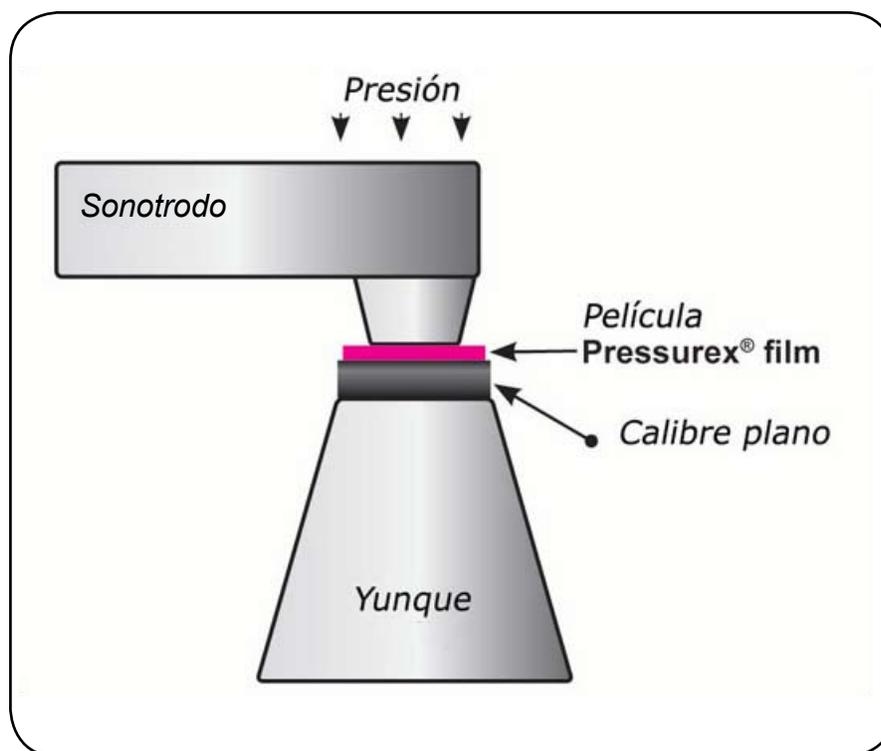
Usa de Pressurex® para configurar de forma óptima una soldadura par ultrasonidos.
